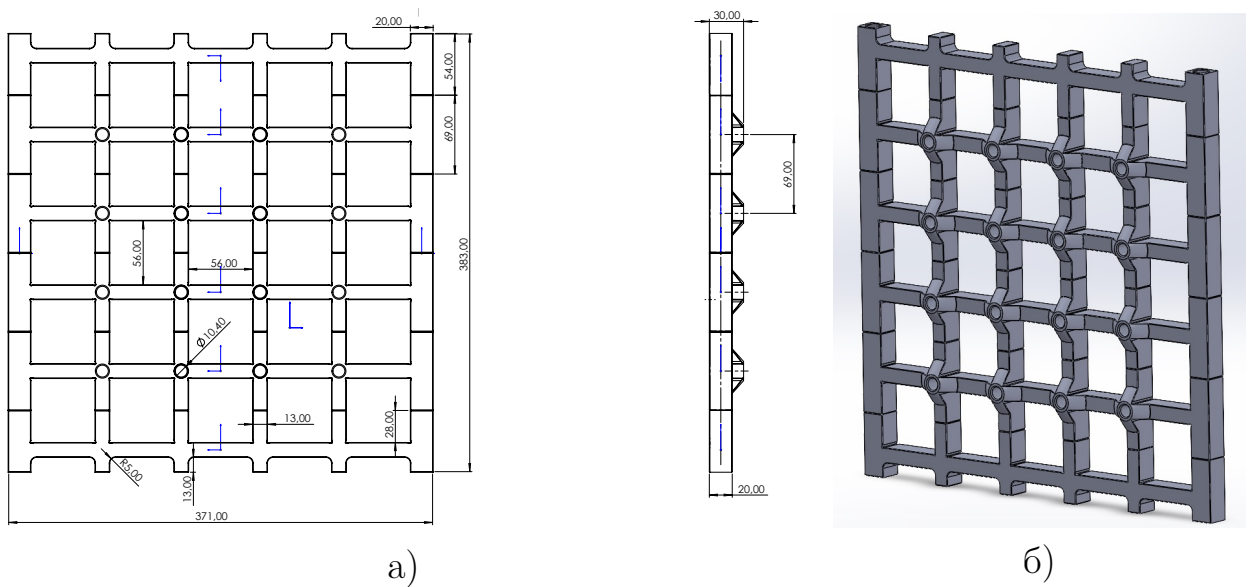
а) Чертеж стойки-матрицы («базы блока»), в которой будут размещаться модули. б) 3D-модель стойки.
